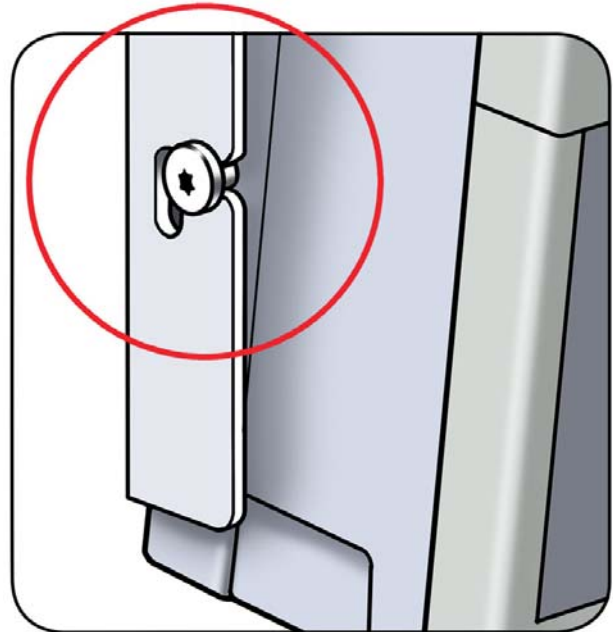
Einführung der Schrauben in die Schlitzte – Detailansicht
